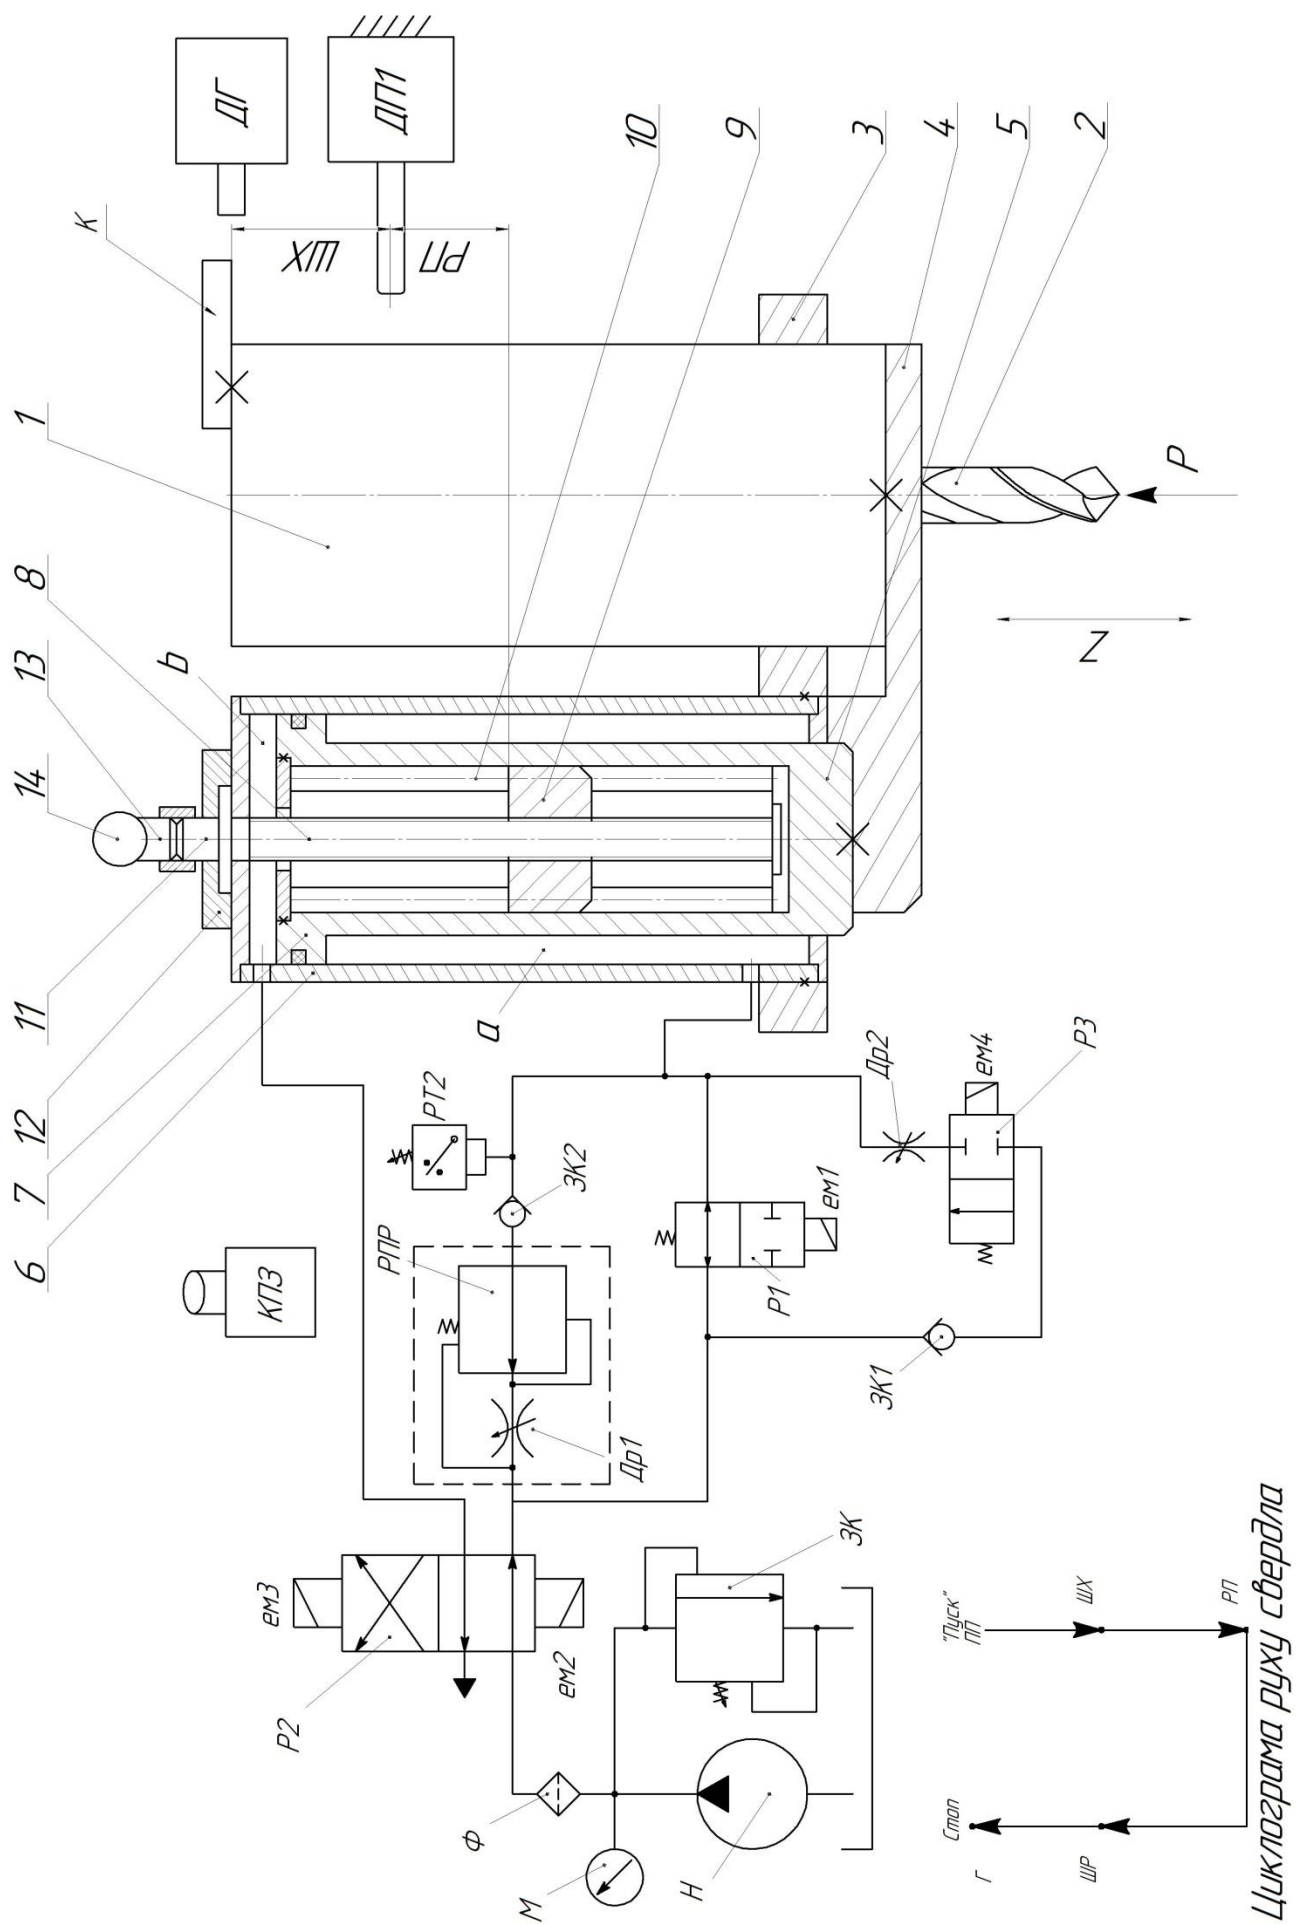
Схема розрахункова приводу осьового переміщення свердла
